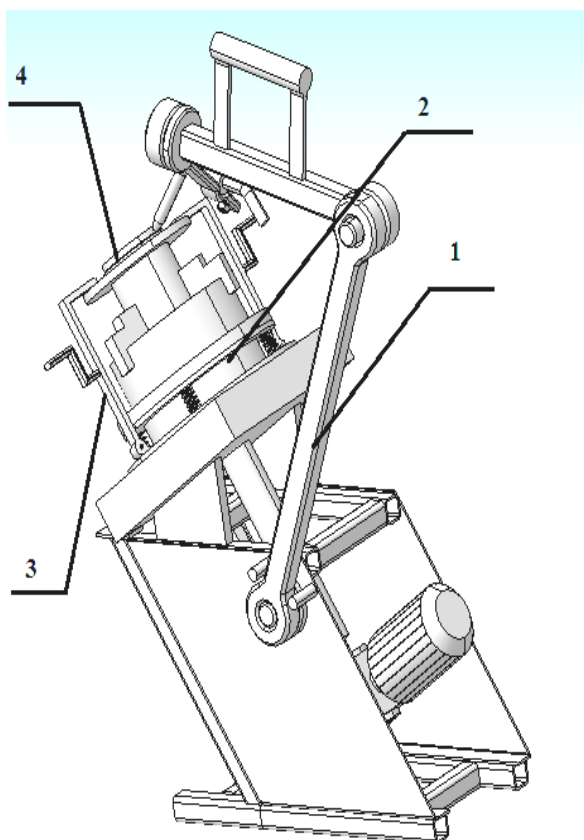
Устройство для сварки дисковых и цилиндрических деталей:
